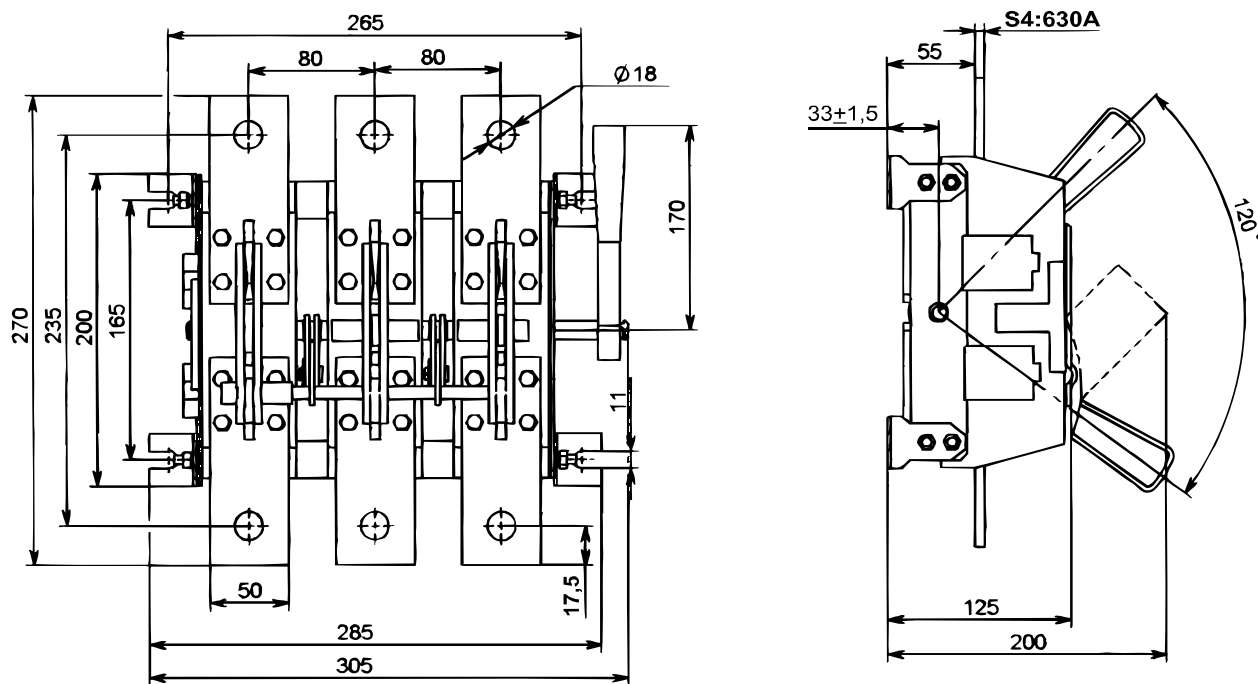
Разъединитель PE19 трехполюсный с боковой ручкой, переднего присоединения шин
